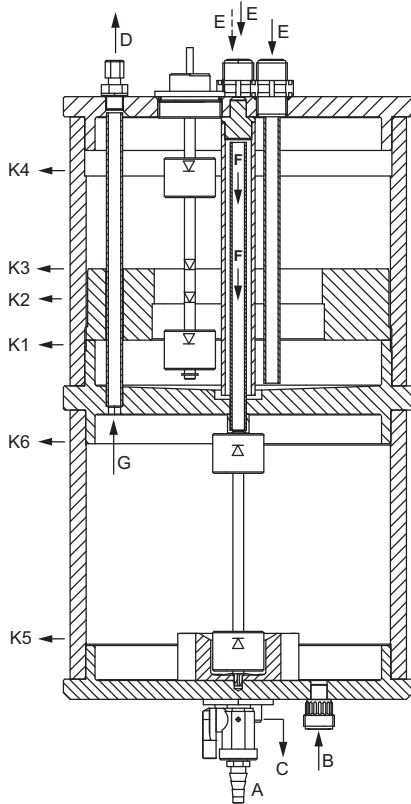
Реактор и внутренний дозирочный резервуар (OCD-162-5/-10/-30)
